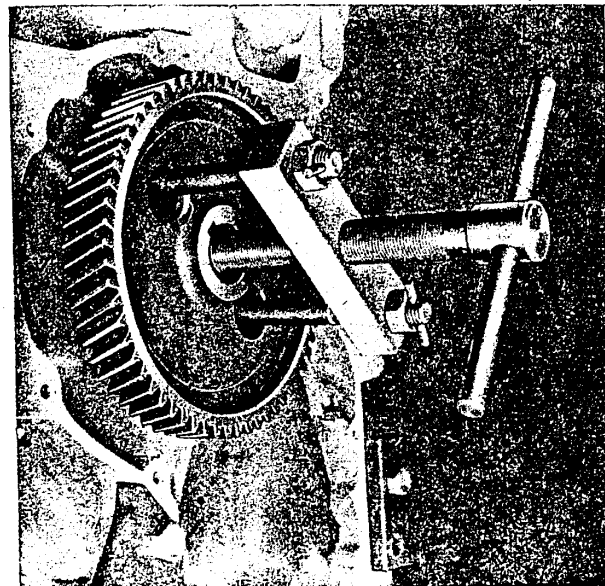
Nockenwellenrad mit Abzieher Werkzeug Nr. 324.020-M 136 abziehen
